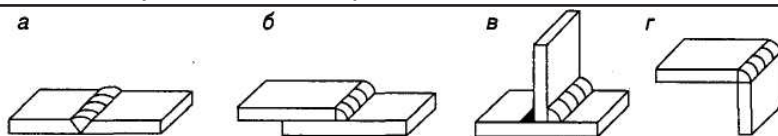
Типы сварных соединений: а-стыковое; б-нахлесточное; в-тавровое; г-угловое.
